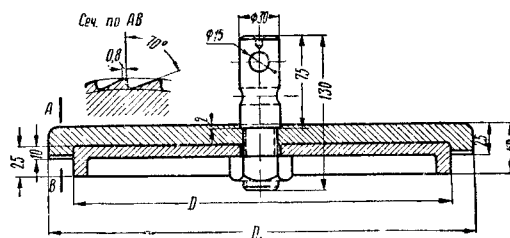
Зенковка с углом 60° для обработки мест присоединения арматуры и труб
